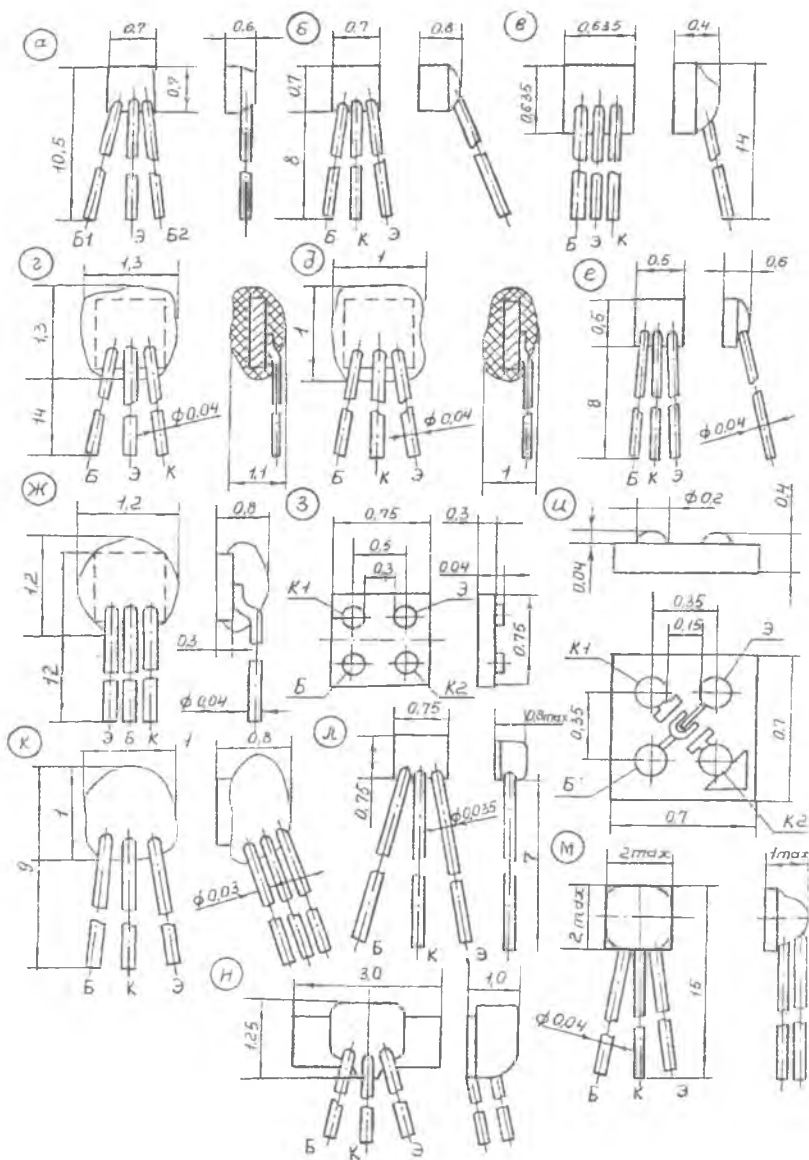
Габаритные чертежи бескорпусных транзисторов типов:
